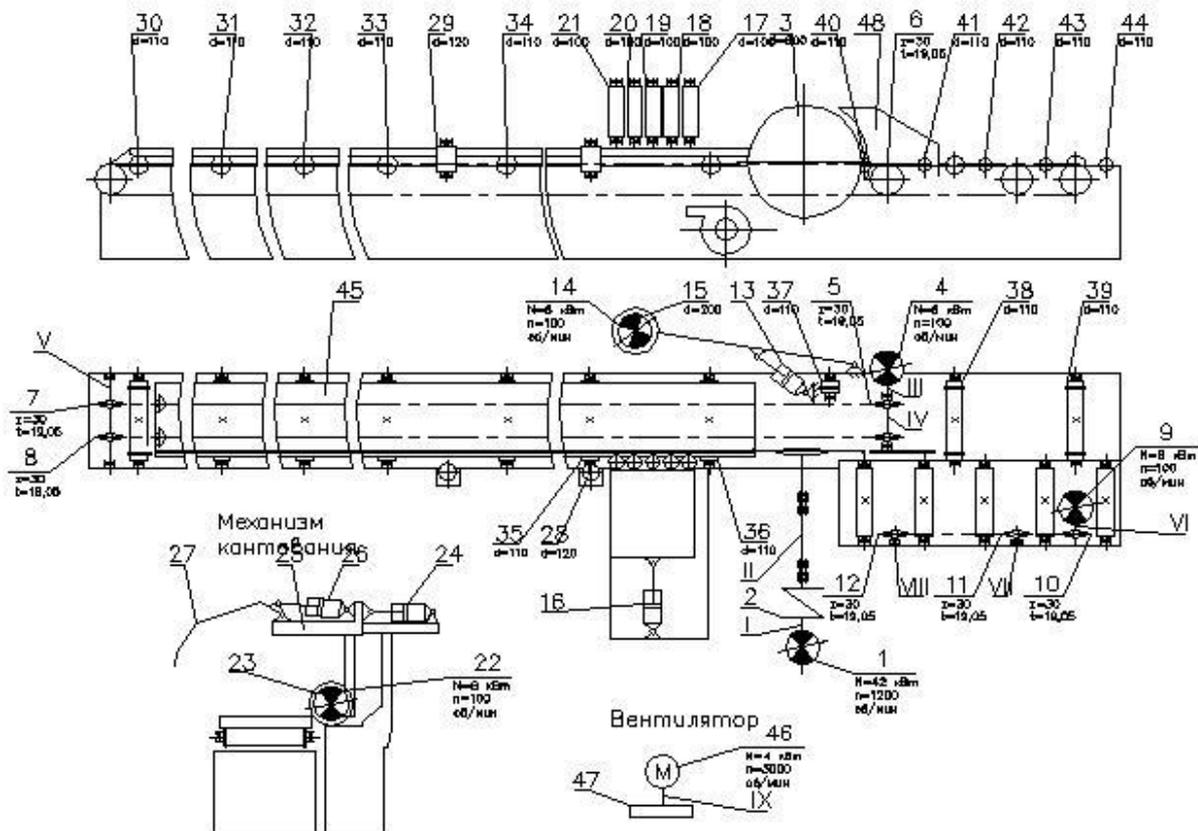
Кинематическая схема круглопильного станка с подвижным
